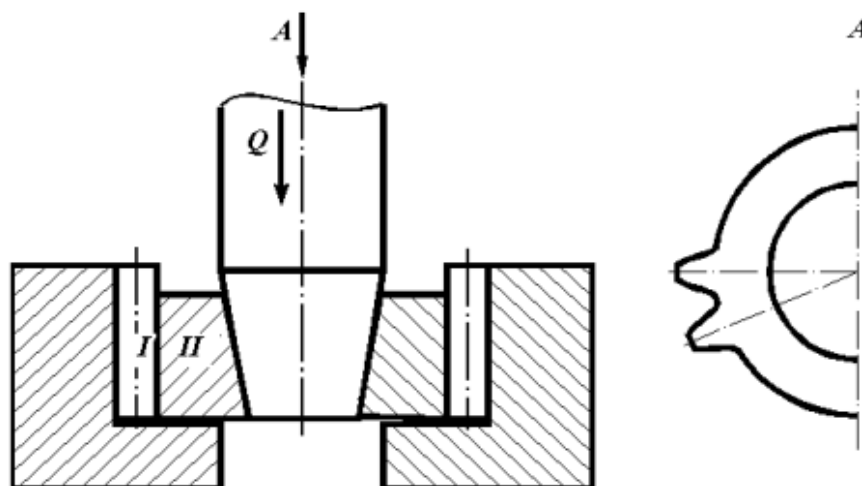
Схема калибровки зубьев шестерни с радиальным течением материала
